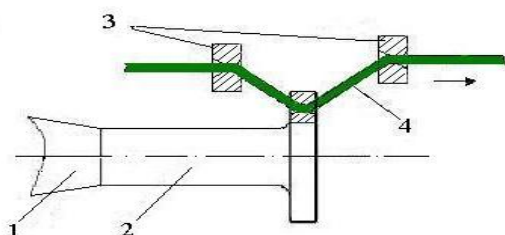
Устройство РКУ протягивания проволоки с наложением ультразвука
